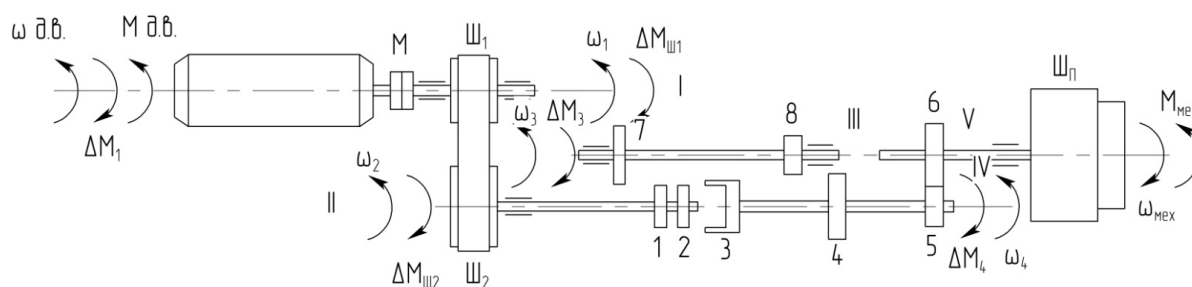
Кинематическая схема механической системы привода главного движения металлорежущего станка
